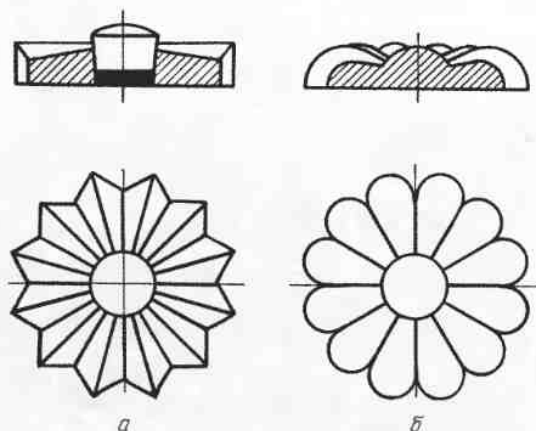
Розетки для ворот: а — выполненные с предварительным пропилом ножовкой сквозных углублений, обработкой ребер ножом и вставкой пробки-заглушки; б — вырезанные из целой дощечки с помощью пилы, ножа и полукруглых стамесок или кругореза
